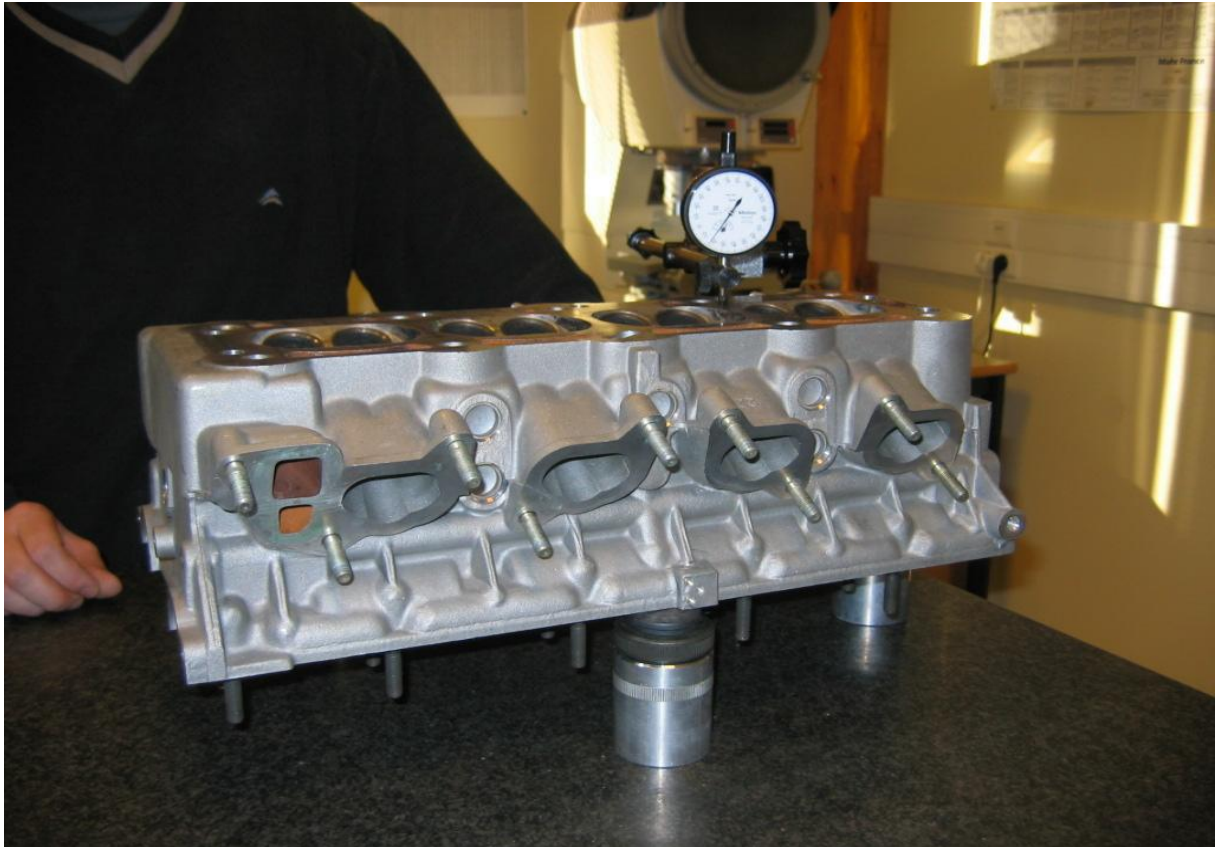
Contrôle de la planéité d'une culasse [9]
